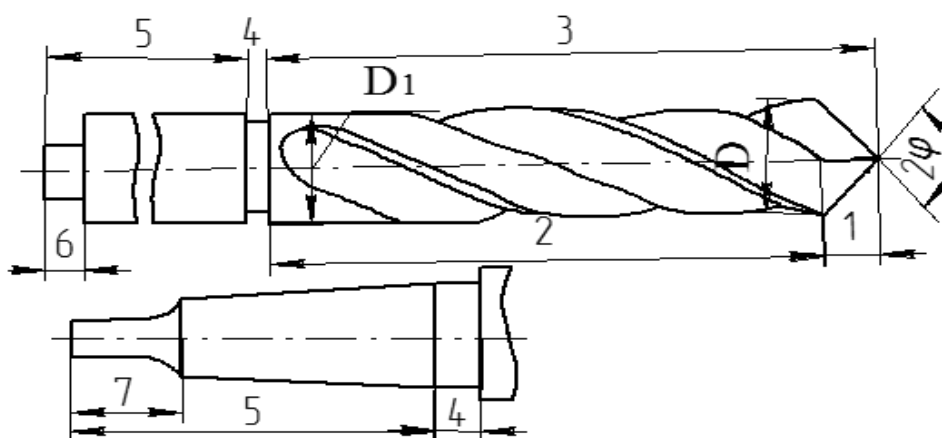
Части спирального сверла: 1 – режущая часть;
